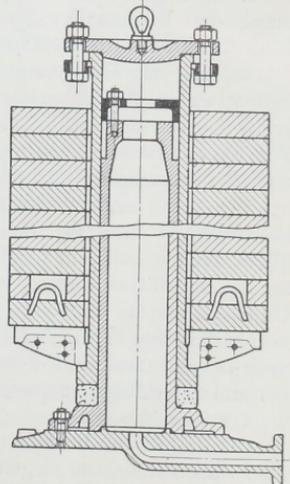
Druckwasserspeicher. Der Zylinder bewegt sich auf einem ruhenden Kolben.
